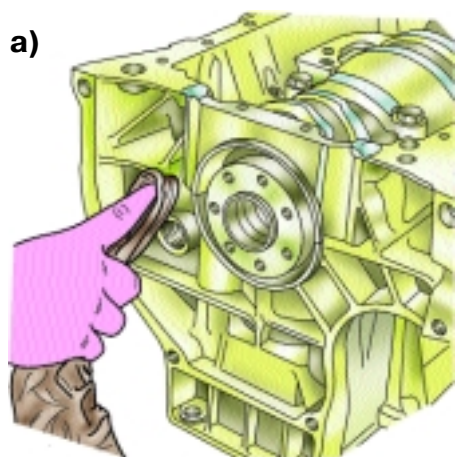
Удаление излишков герметика с крышки 1-го коренного подшипника коленчатого вала двигателя F3R 272
